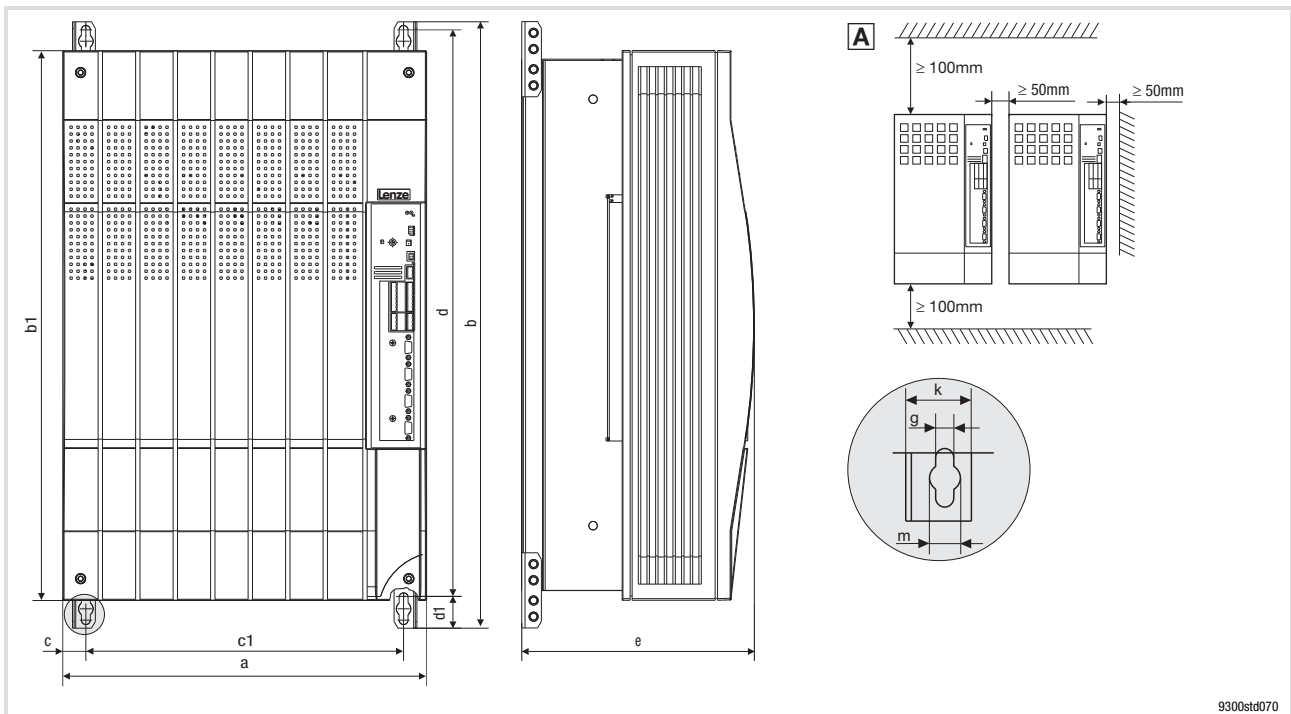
Standardmontage mit Befestigungswinkeln 55 ... 75 kW
